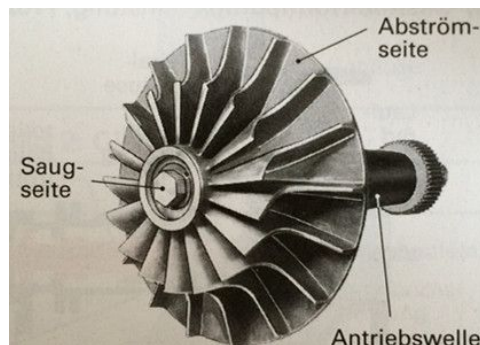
Pumpenlaufrad (Quelle: aus dem Buch: Chemietechnik)
